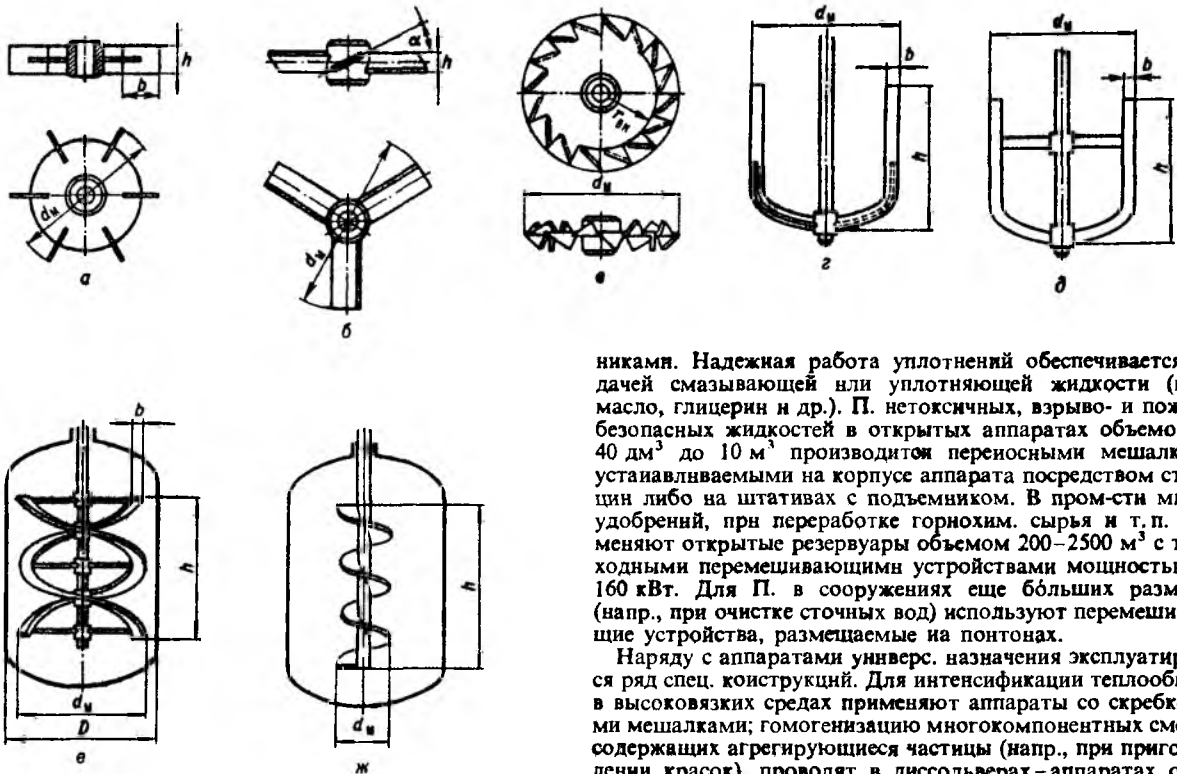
Конструкции мешалок: а - турбинная; б - трехлопастная; в - фрезерная; г - якорная; д - рамная; е - ленточная; ж - шнековая.
